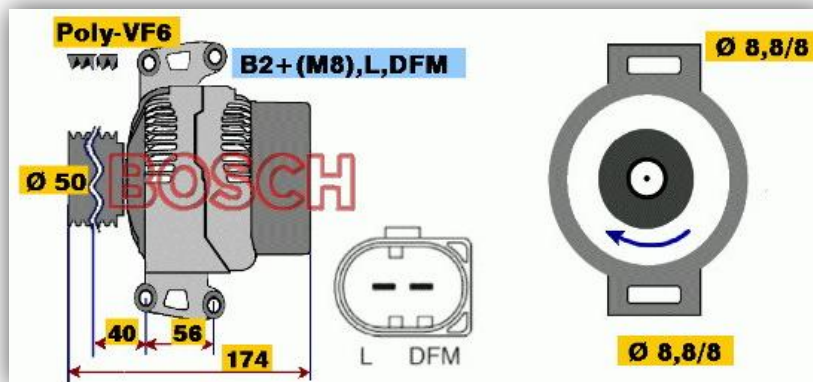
Características técnicas do alternador BOSCH 0 124 625 019
